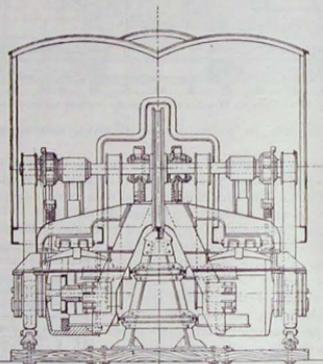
Ferrovia Liverpool-Manchester - Gruppo motore.
